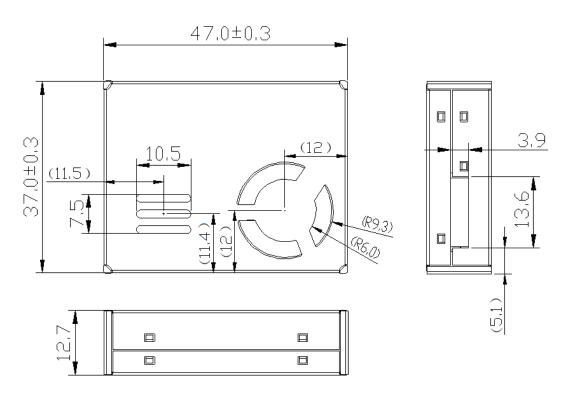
外观尺寸图(单位: mm, 未标注公差: ±0.2mm)
